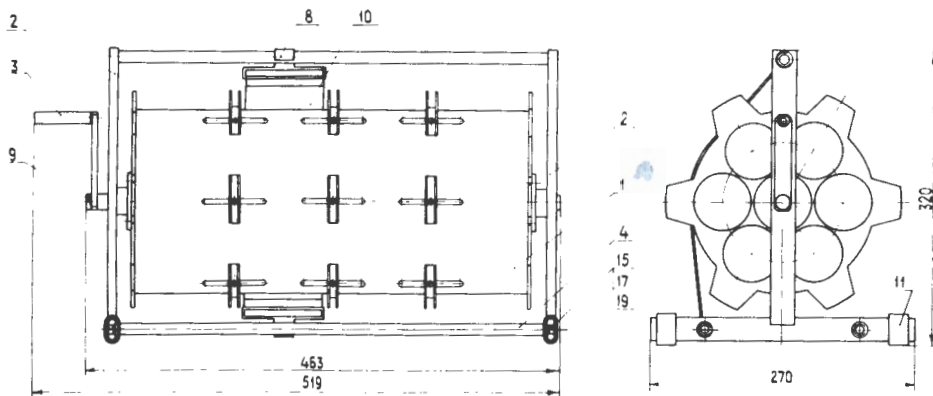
Конструкция кабельного барабана: 1 — барабан с подвижными секциями; 2 — стойка; 3 — ручка; 4 — упор; 5 — фиксатор натяжения; 9 — винт; 10 — резиновый пояс; 11 — амортизатор; 15,17,19 — элементы основания.
